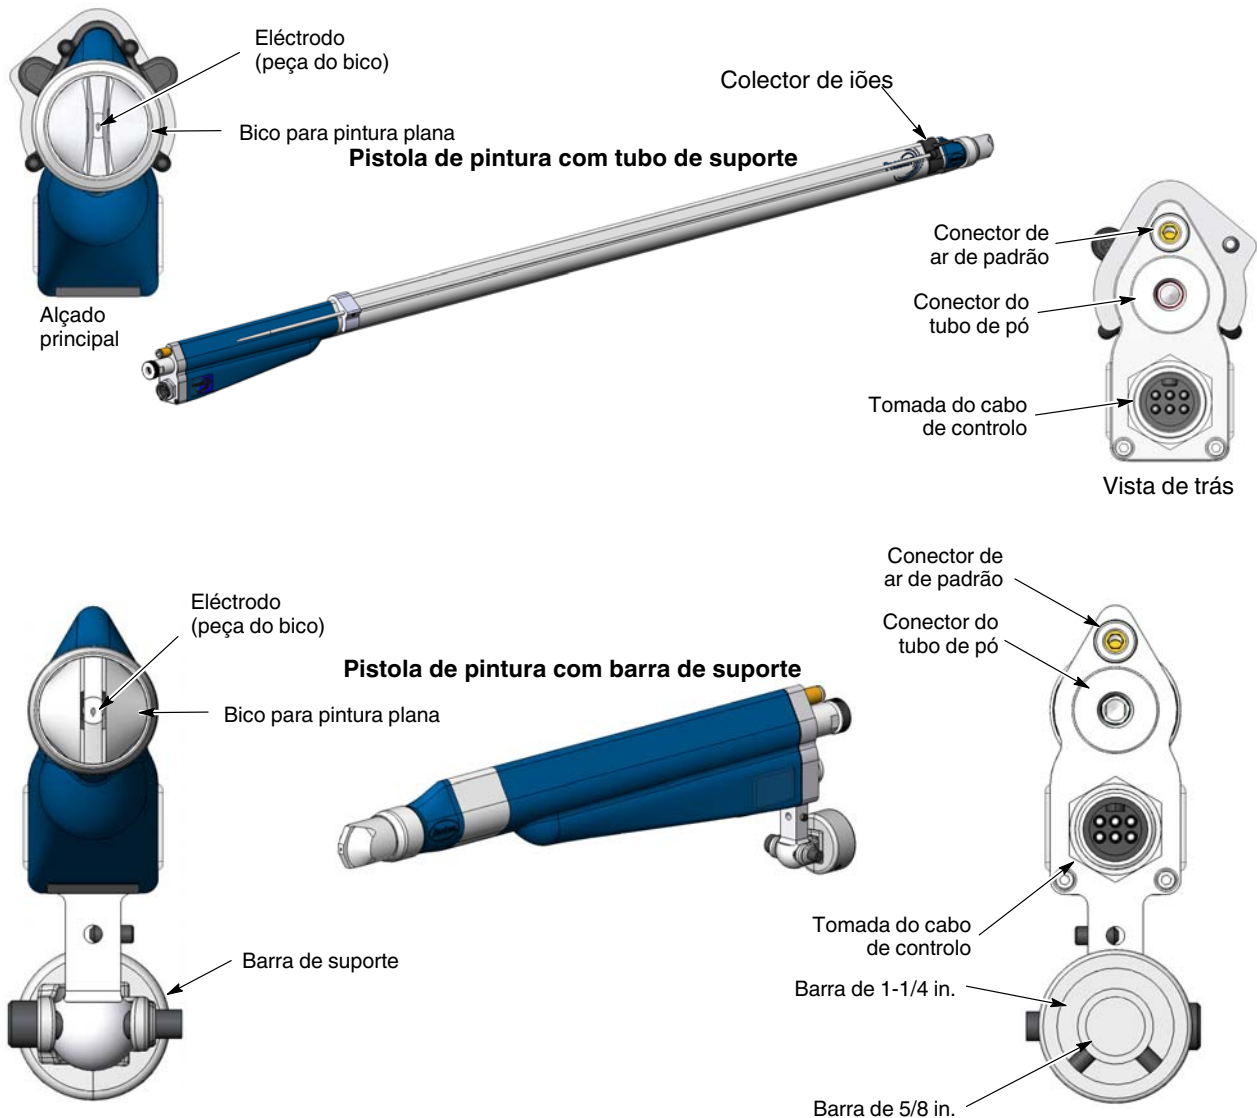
Pistolas automáticas de pintura com pó Prodigy
